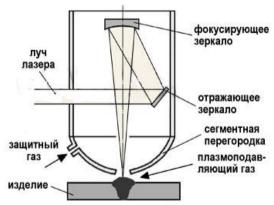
Процесс лазерной сварки¹⁰⁴
